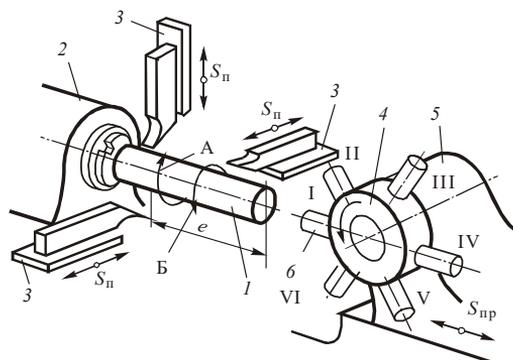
Схема работы токарно-револьверного станка-автомата:
